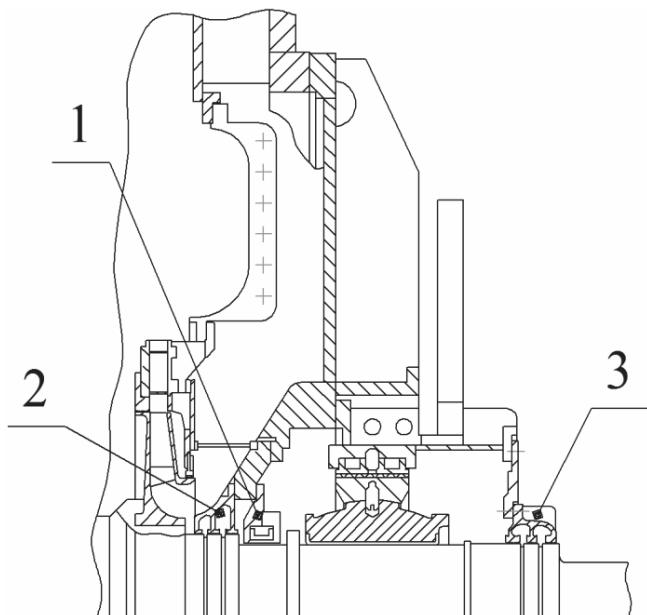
Уплотнительные узлы в ТГ с избыточным давлением внутри корпуса:
